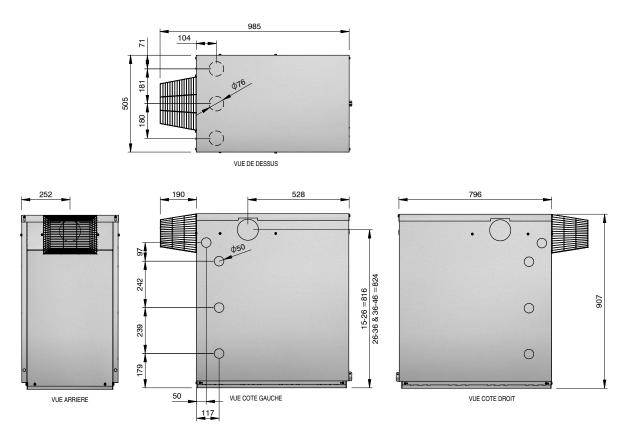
Dimensions Vortex Bas NOx Outdoor 24kW et Outdoor 32kW
